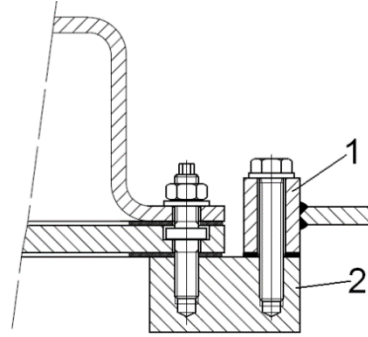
Disposición de montaje en la parte inferior con pernos del collar.
